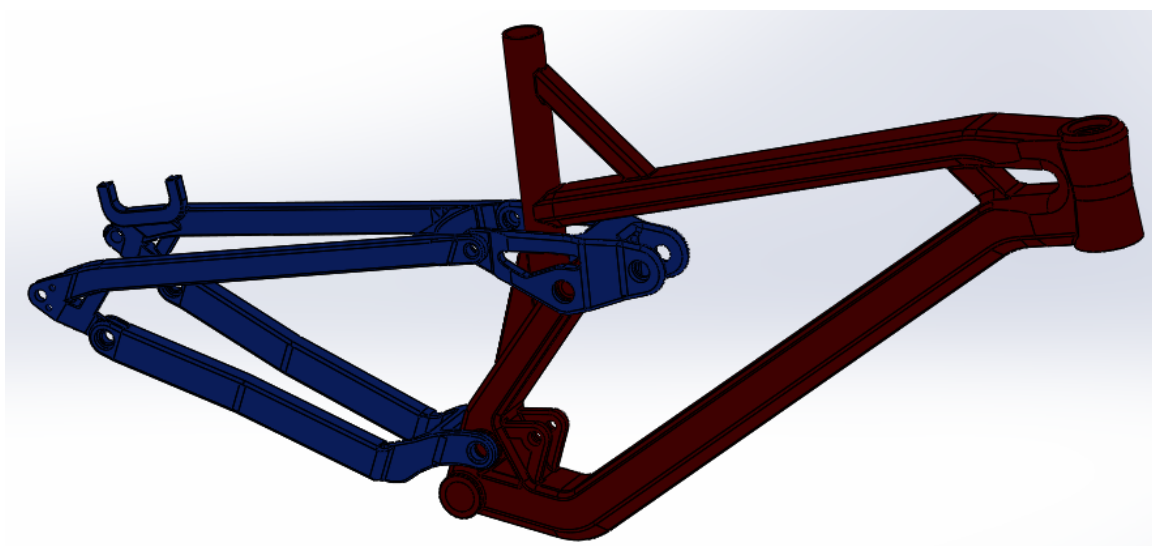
Assemblatge de les quatre parts que integren el quadre amb Solid Works
